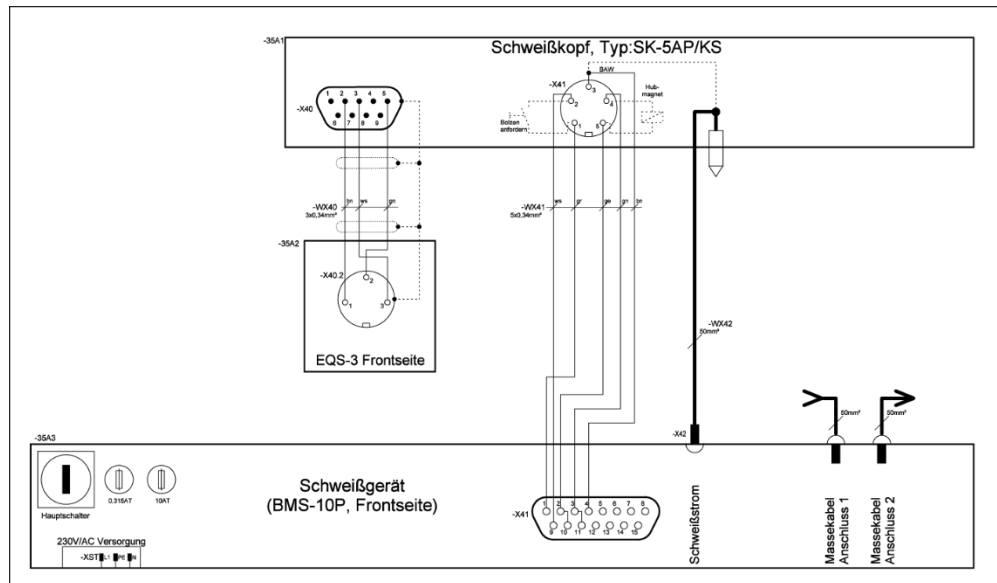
Anschlussschema Bolzenschweißkopf mit BMS-10P und EQS-3
